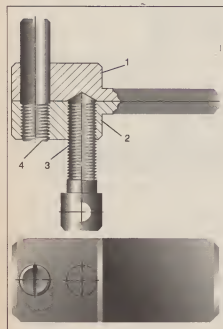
Приспособление для "разработки" поршней без винта с левой резьбой: 1, 2 — лапки; 3 — винт; 4 — направляющий палец.
